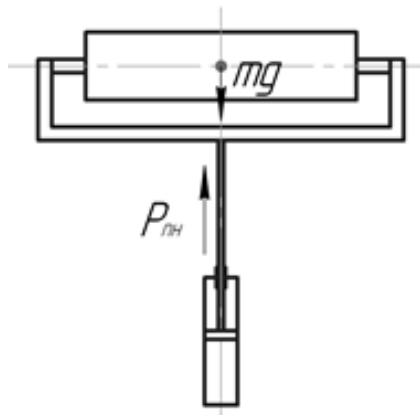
Розрахункова схема для підбору пневмоциліндра упора
